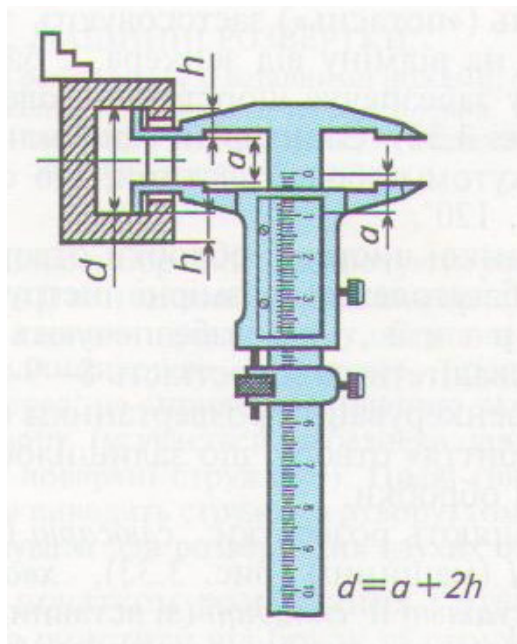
Контроль діаметра виточки за допомогою штангенциркуля зі спеціальними губками
